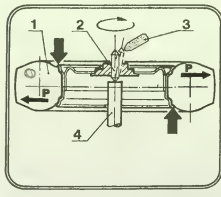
Динамическая балансировка колеса: 1 — колесо; 2 — приспособление; 3 — мелок; 4 — опора; большими стрелками показаны места установившихся грузиков; Р — силы, создающие динамический дисбаланс.
